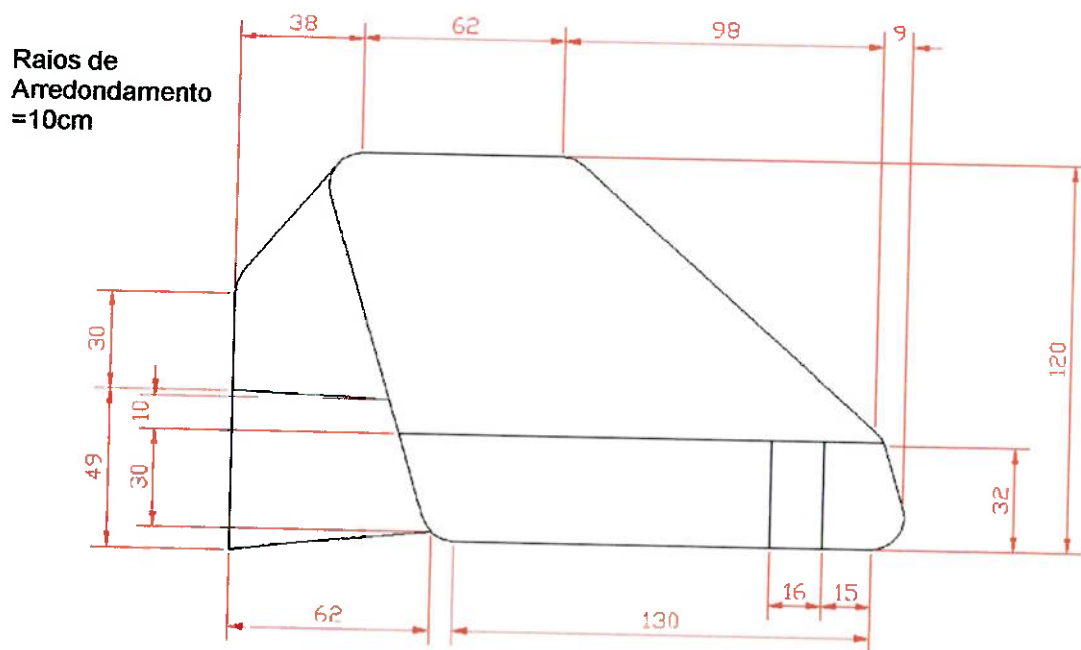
VISTA LATERAL DO VEÍCULO MINI-BAJA (MEDIDAS EM CM)
